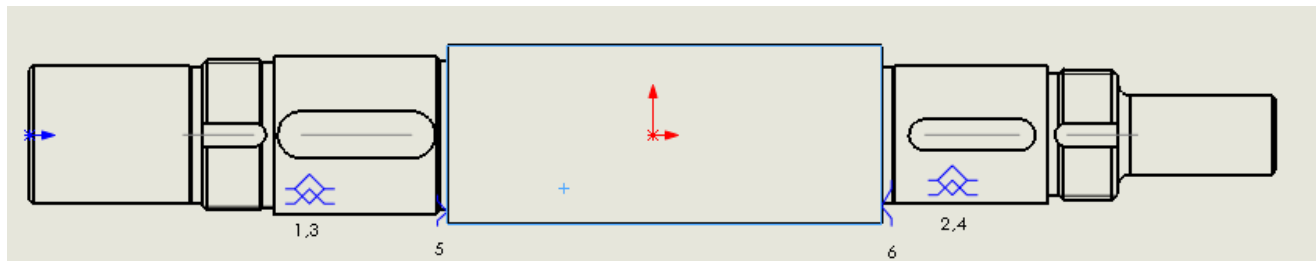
Теоретична схема базування фрезерного установу на пристрої
